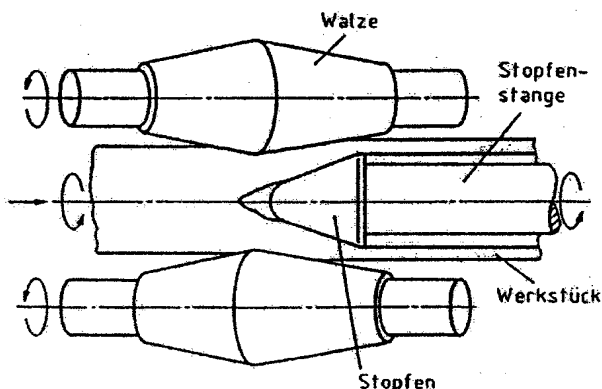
Schrägwalzen mit doppelkegeligen Walzen (Stopfenwalzwerk zur Rohrherstellung).
